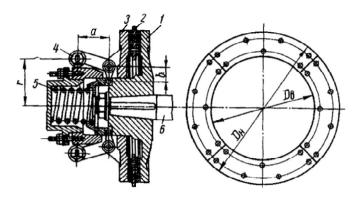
Скоростной дисковый тормоз: 1 – диск вращающийся с валом; 2 – неподвижный диск; 3 – диск; 4 – тормозной груз; 5 – регулировочная пружина; 6 – вал
